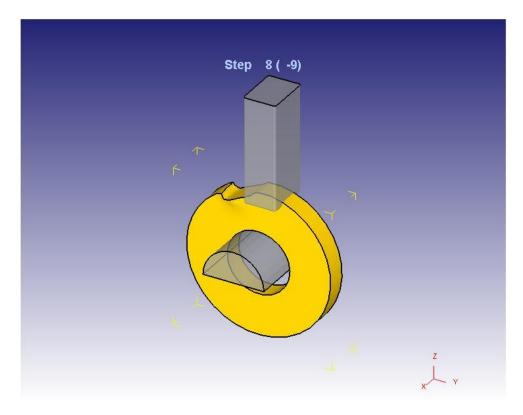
Положение заготовки после операции поворота вокруг оси X
